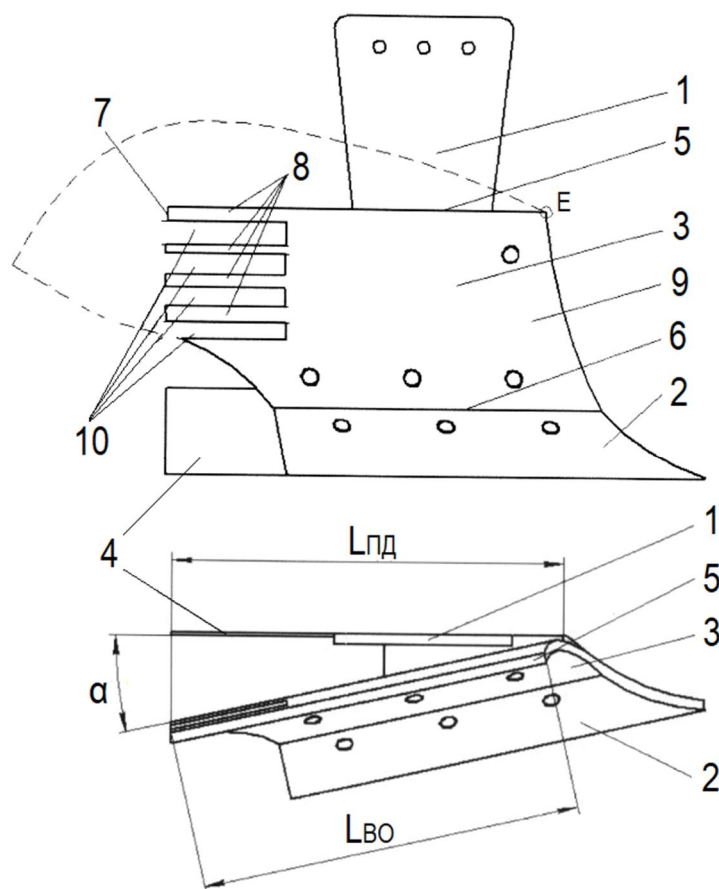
Экспериментальный корпус плуга в двумерной проекции: 1 – стойка; 2 – лемех; 3 – отвал; 4 – полевая доска; 5 – верхний обрез; 6 – нижний обрез; 7 – кромка рабочей поверхности; 8 – полосы; 9 – грудь отвала; 10 – прямоугольные вырезы; L_{во} – длина верхнего обреза отвала; L_{пд} – длина полевой доски
